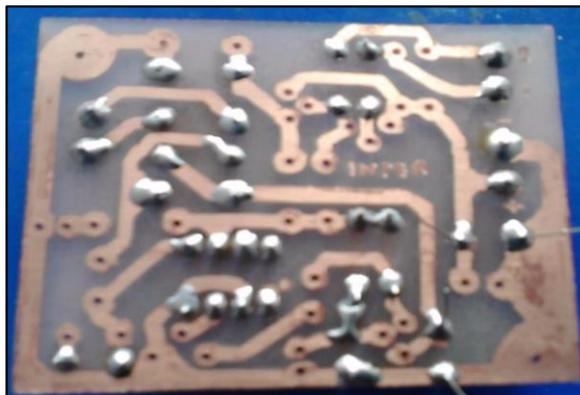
Foto posterior del circuito impreso (Lado soldaduras).
